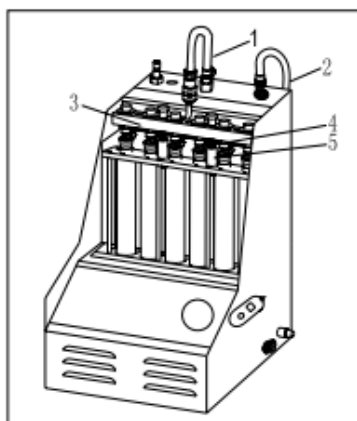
1-Шланг; 2-Кабель управления форсунками; 3-Распределитель топлива; 4-Шпильки; 5-Рифленая гайка.
